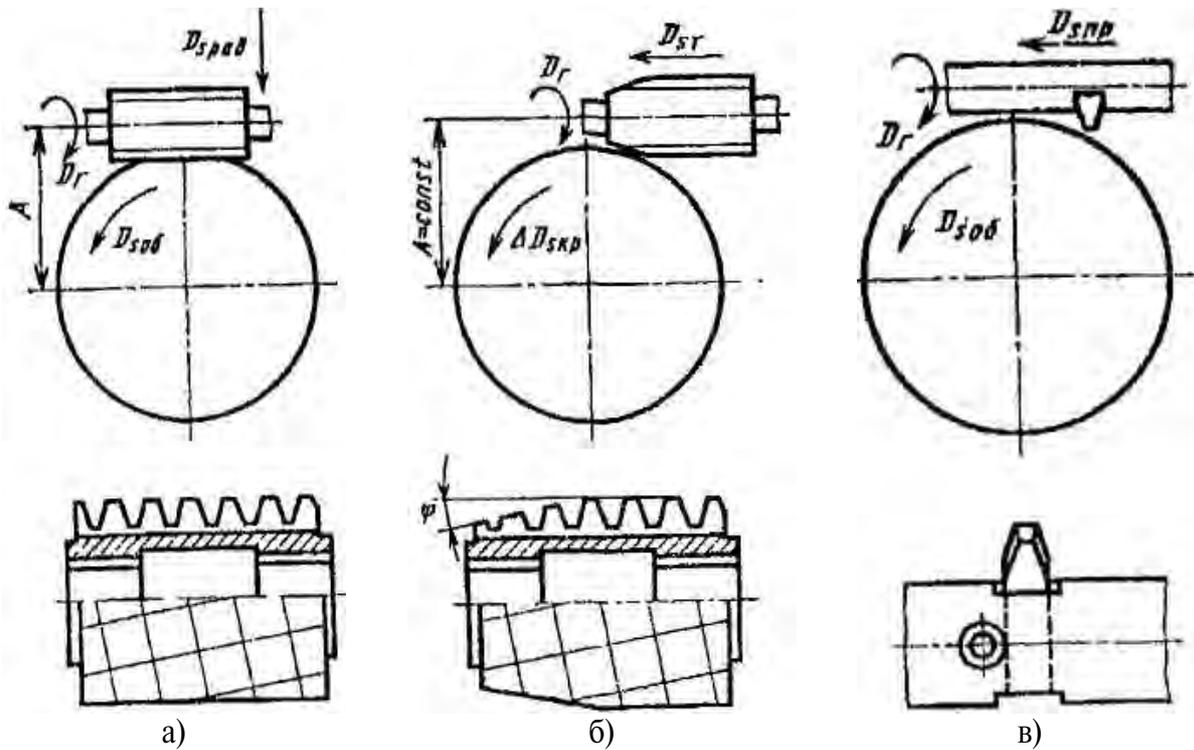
Схемы обработки и инструменты для нарезания червячных колес
